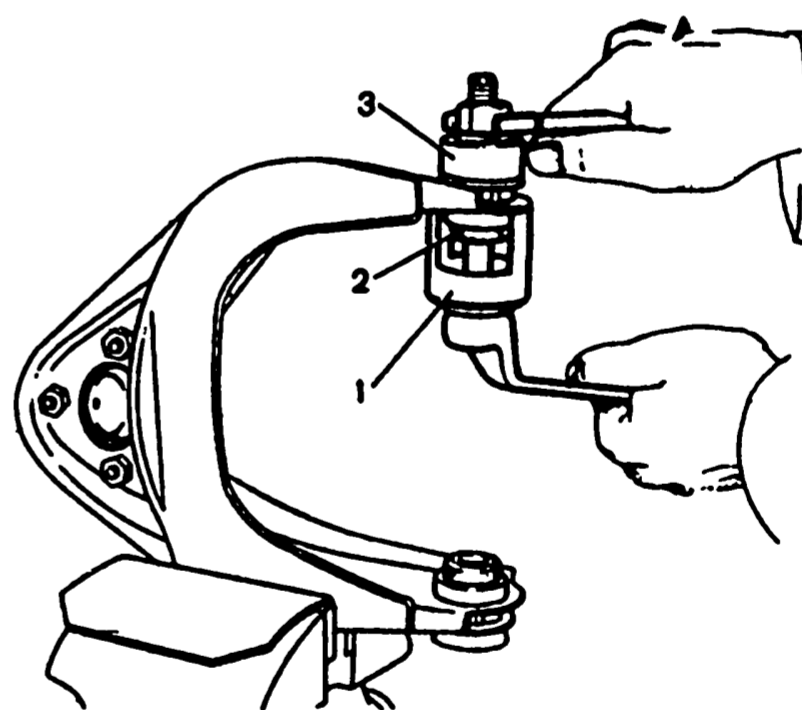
Запрессовка шарниров верхнего рычага: 1 - приспособление А.47046; 2 - шарнир; 3 - колпачок, применяемый вместе с приспособлением А.47046
